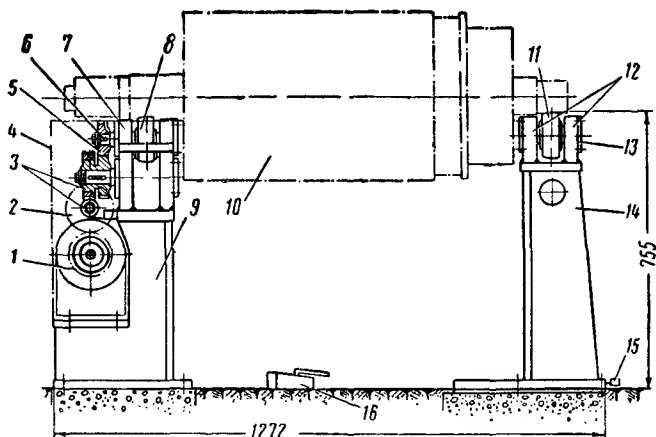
Приспособление для поворота якоря электрической машины: 1 — электродвигатель; 2, 5 — цилиндрические шестерни; 3 — червячная пара; 4 — кожух; 6 — валек опорного ролика; 7, 12 — корпуса подшипников; 8 — опорный ролик ведущий; 9 — передняя стойка; 10 — якорь; 11 — опорный ролик ведомый; 13 — крышка; 14 — задняя стойка; 15 — червячный винт; 16 — ножная педаль управления
